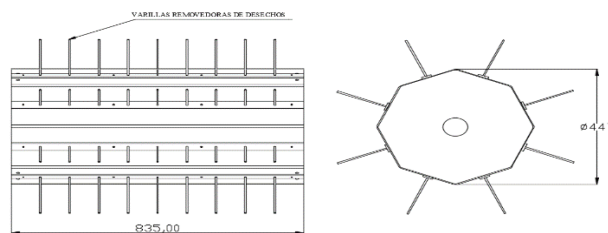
Dimensiones geométricas del cilindro removedor de granzas
